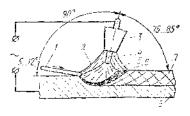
Схема ручной аргоподуговой сварки с присадочным прутном
